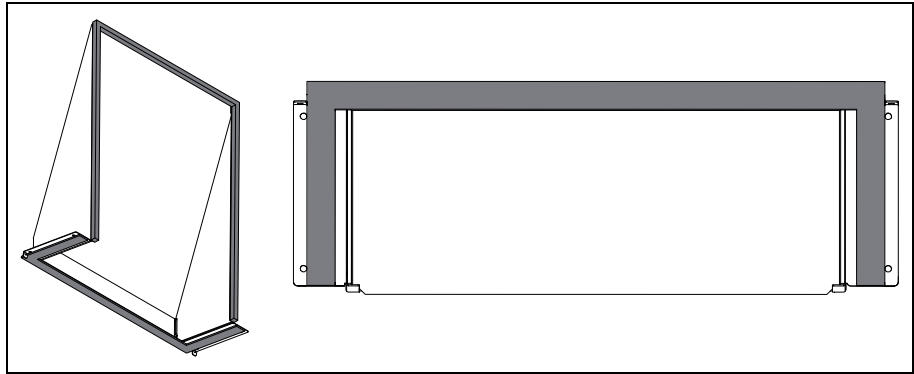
Dichtung an Anlagefläche Vertikalteil zu Horizontalteil
